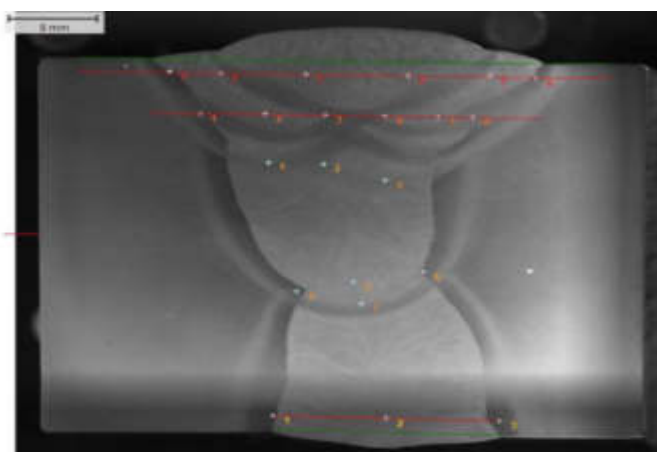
Шлиф после сварки с применением двух дуг
